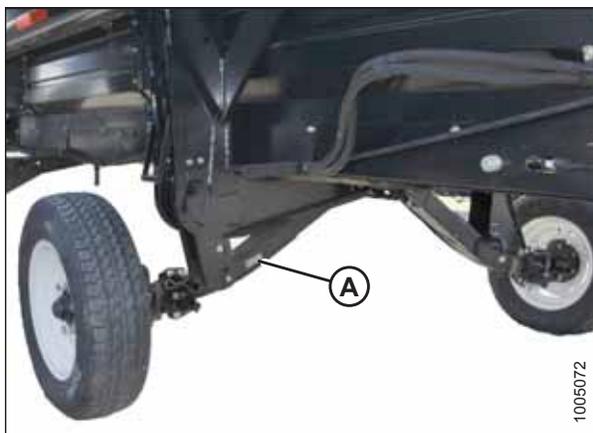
Расположение опорно-транспортных/стабилизирующих колес
